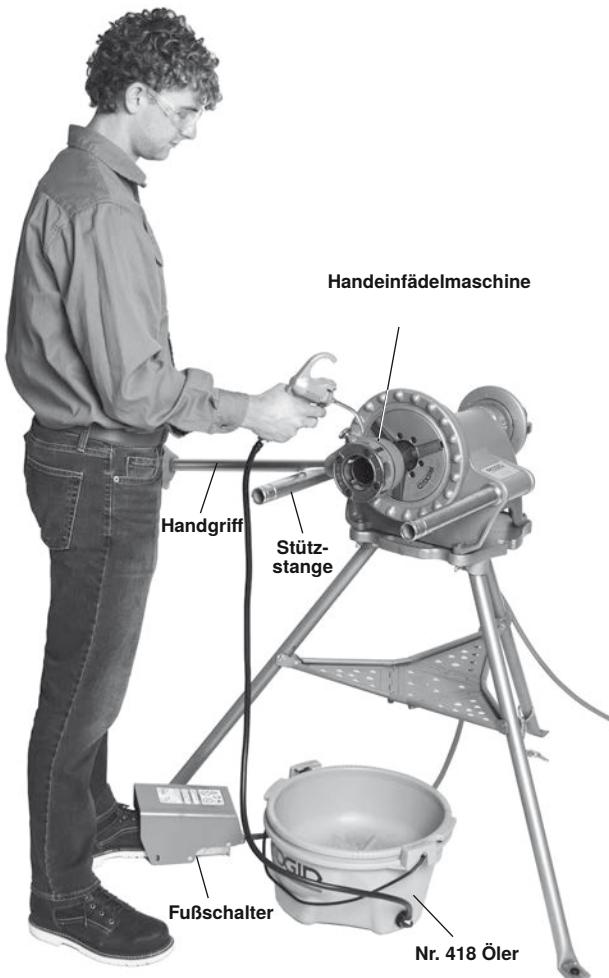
Gewindeschneiden mit Handgewindeschneidmaschinen/Richtige Betriebsposition (Griff der Gewindeschneidmaschine in Kontakt mit der Stützstange halten.)
